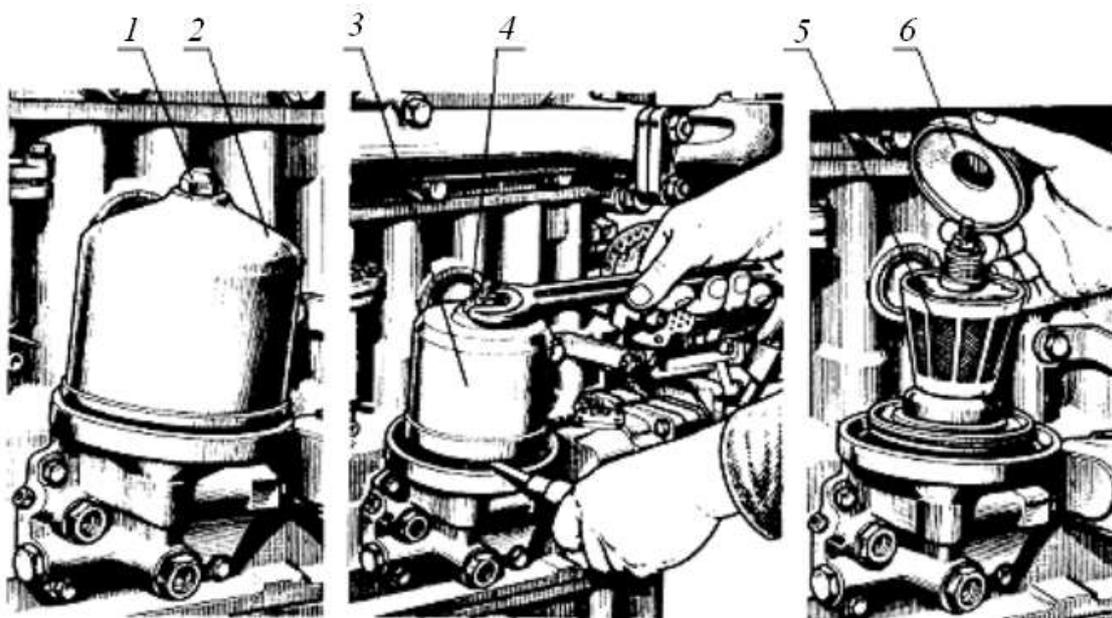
Очистка ротора центробежного масляного фильтра:
